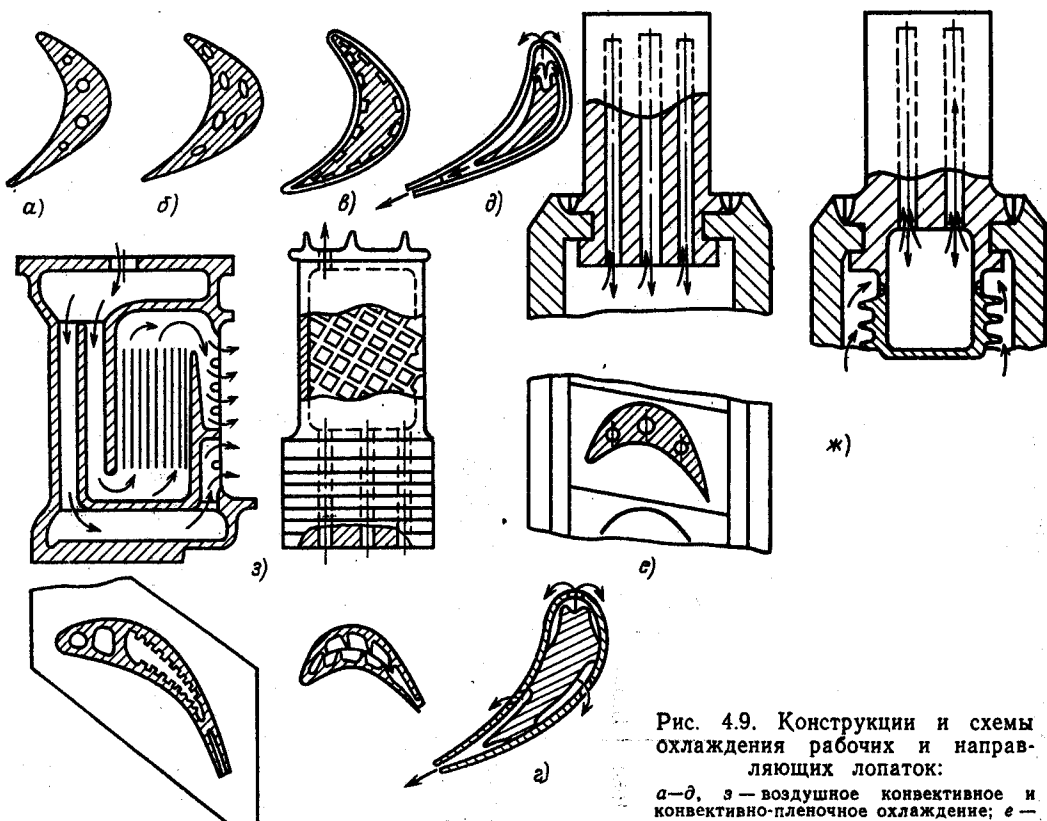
Конструкции и схемы охлаждения рабочих и направляющих лопаток:
